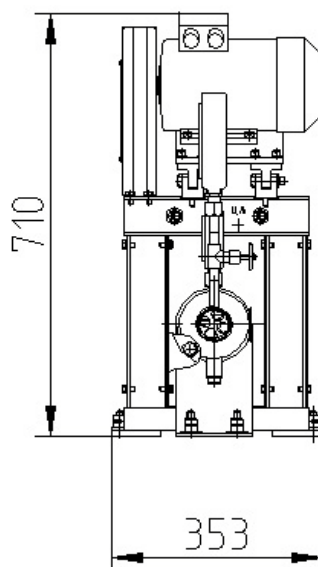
Габаритный чертеж газодувки KUK10AN001, KUK20AN001, KUK30AN001, KUK40AN001
